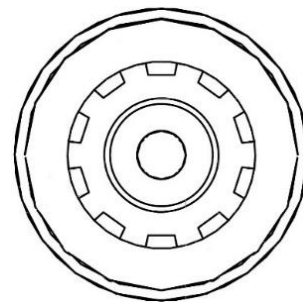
Vista planta A-A, del tapón sólido con el nuevo rediseño.
